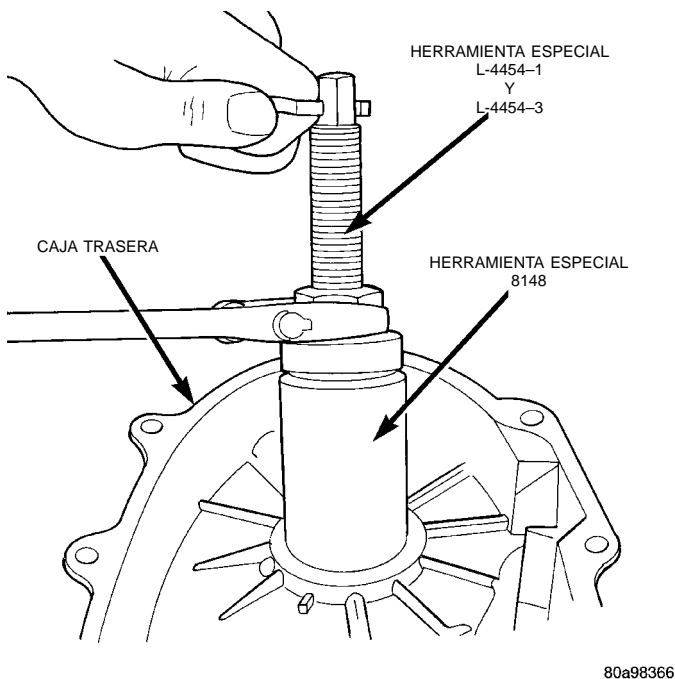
Retiro del cojinete trasero del eje transmisor delantero
